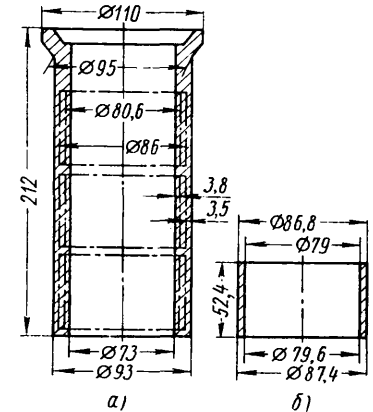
Основные размеры заготовок нирезистовой гильзы, получаемых центробежным способом (а) и литьем в оболочковые формы (б)
